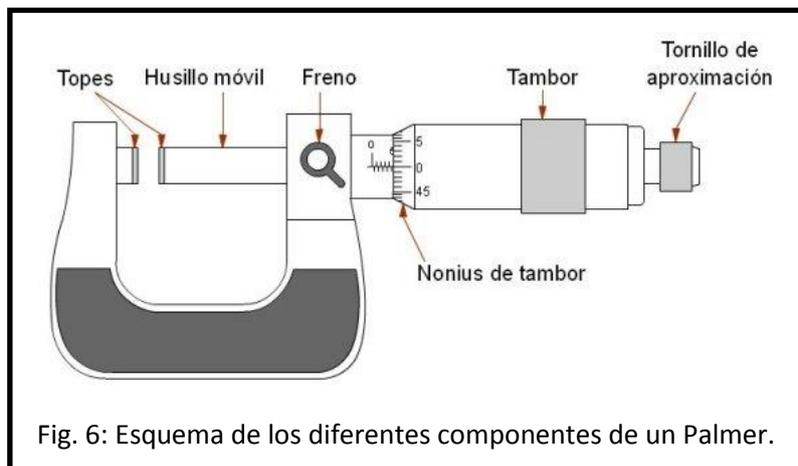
Esquema de los diferentes componentes de un Palmer.
